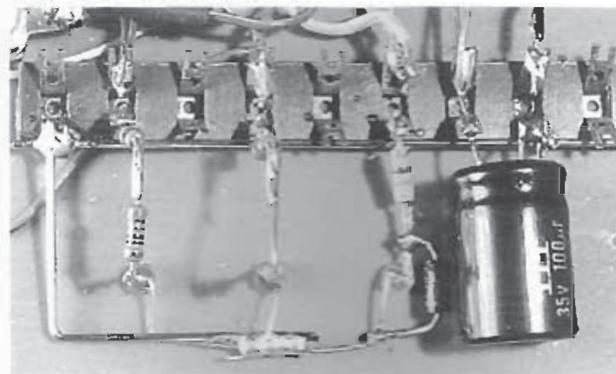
Listón de soldadura como serie de puntos de empalme eléctricos.
